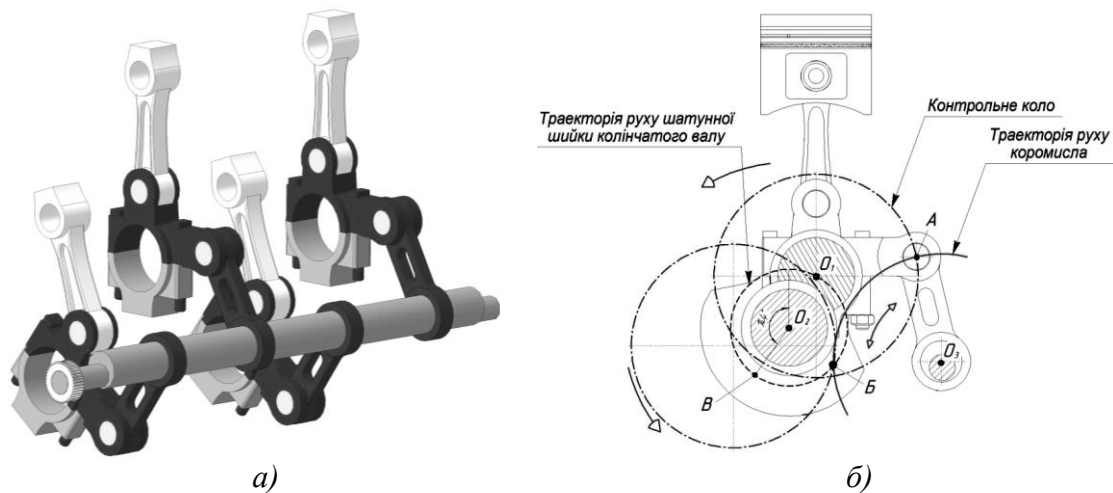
Траверсний механізм (а) і його кінематика (б):  $O_1$  – центр шатунної шийки;  $O_2$  – центр корінної шийки;  $O_3$  – центр нижньої головки коромисла; А – верхнє положення верхньої головки траверси; Б – нижнє положення верхньої головки коромисла; В – положення шатунної шийки, при якому верхня головка коромисла починає рухатись з положення Б в положення А.
